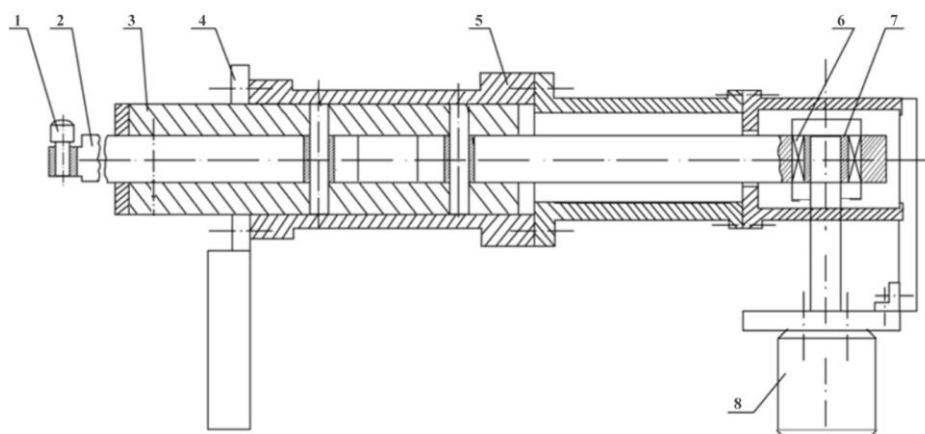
Принципова схема пристрою для вібраційного обкатування зовнішніх циліндричних поверхонь: 1 – алмазний вигладжувач, 2 – тяга, 3 – державка, 4 – планка, 5 – корпус, 6 – підшипник, 7 – змінний ексцентрик, 8 – електродвигун з ротором
